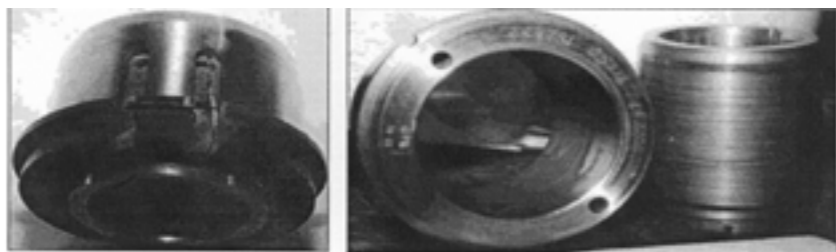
Фрезерованные пазы для гидростатического подвода конденсата (слева)
